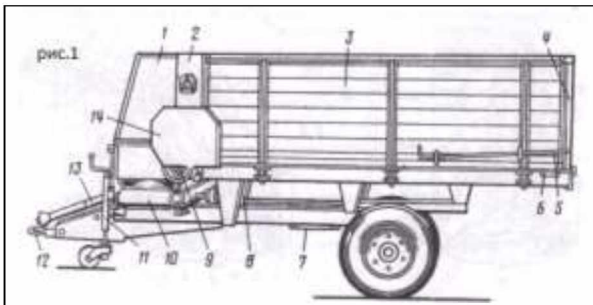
Малогабаритний кормороздавач РММ-6
